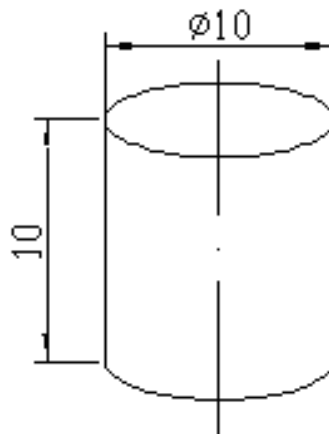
Форма и размеры уплотнительного материала (столбик)
